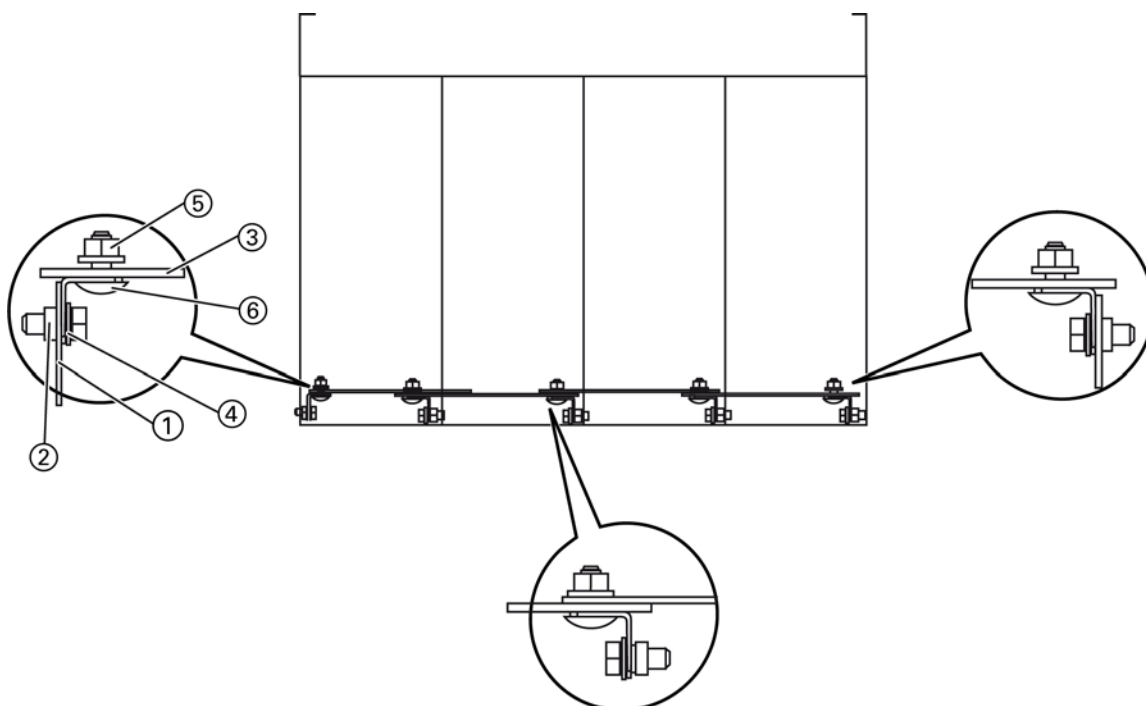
Резьбовое соединение сборной шины заземления (вид сверху)
